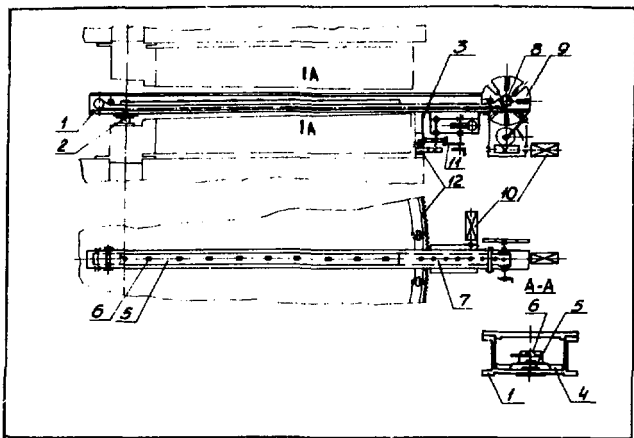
Принципиальная кинематическая схема магнитометра. 1 - штанга, 2 - поворотная опора, 3 - тележка, 4 - направляющие, 5 - каретка, 6 - датчики Холла, 7 - лента, 8 - цевочный барабан, 9 - мальтийский восьмизаходный механизм, 10 - безстаторный электродвигатель, 11 - шестизаходный мальтийский механизм, 12 - шестерня.
